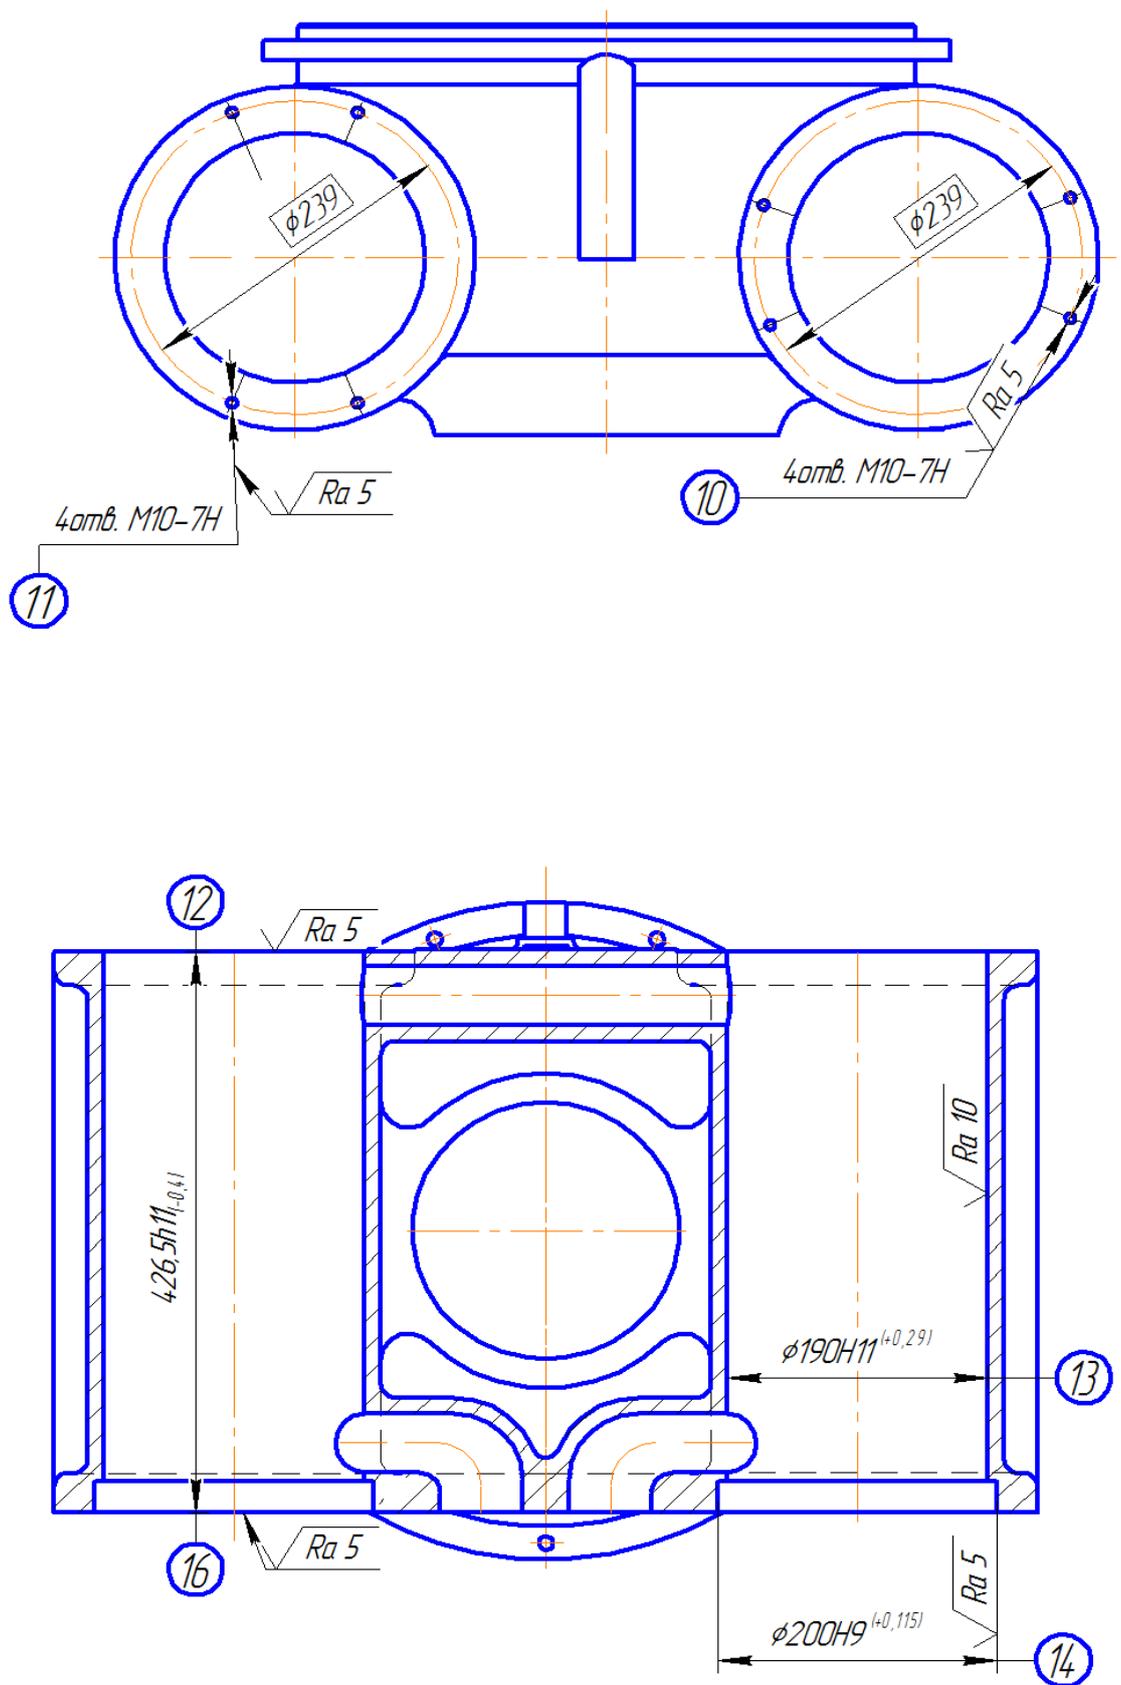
Эскиз детали «Корпус водомасляного охладителя»
